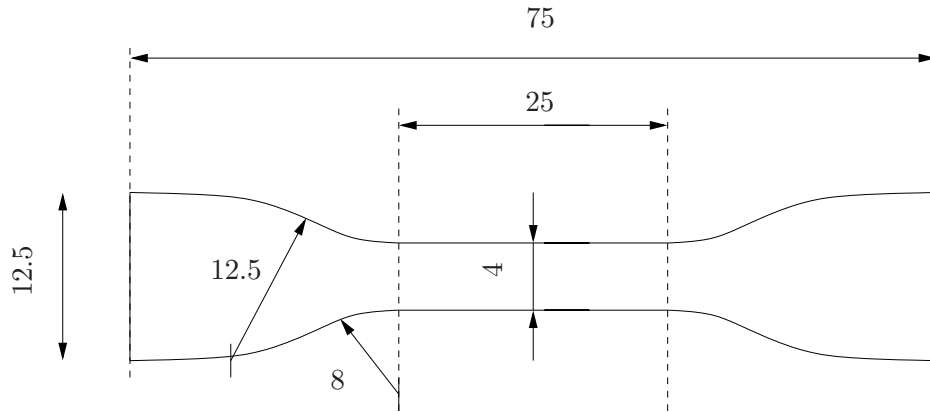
Dimensions éprouvette haltère type H2 (mm).
